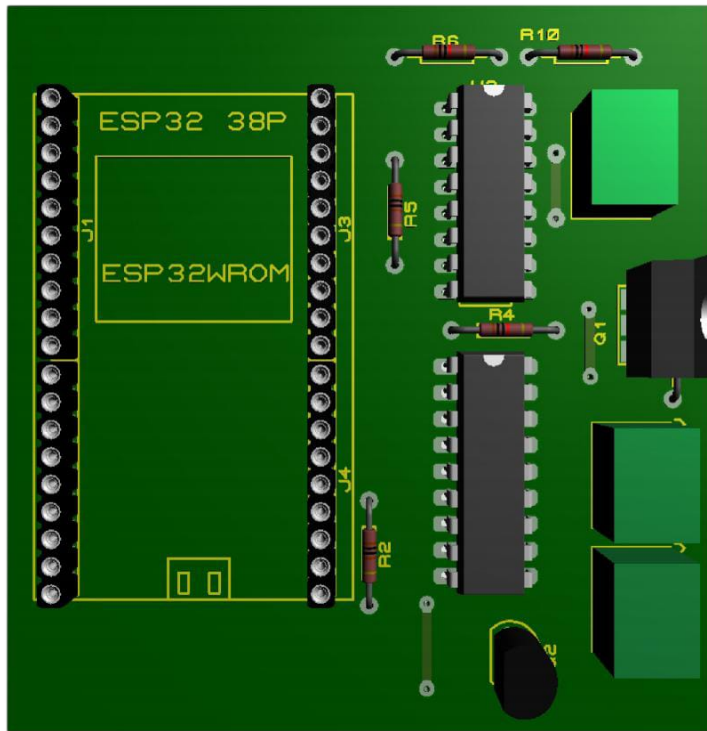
Diseño 3D de Placa PCB. Autor propio.
